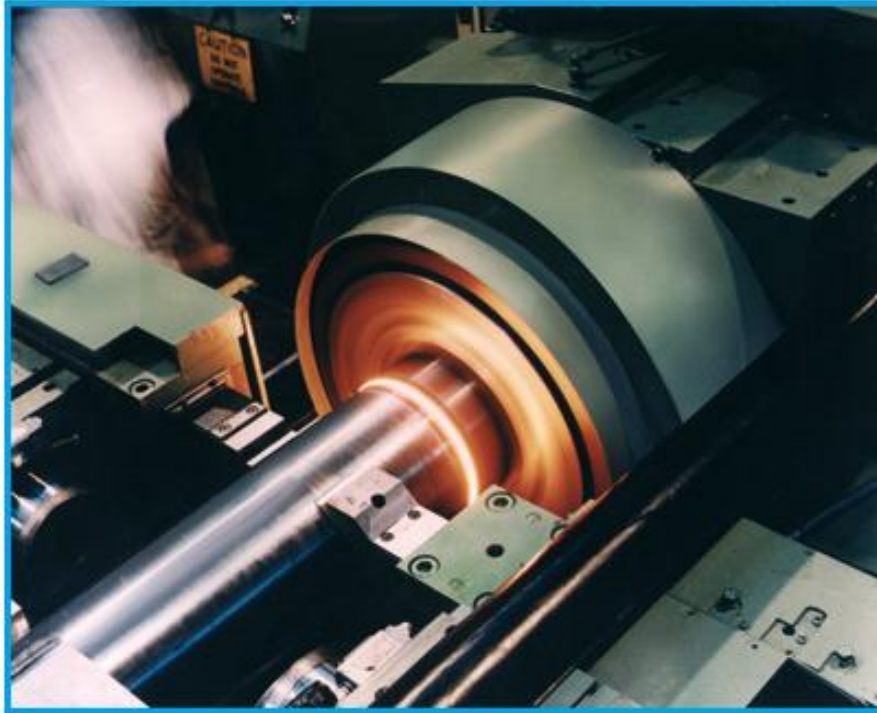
Máquina soldadora por fricción por inercia.
